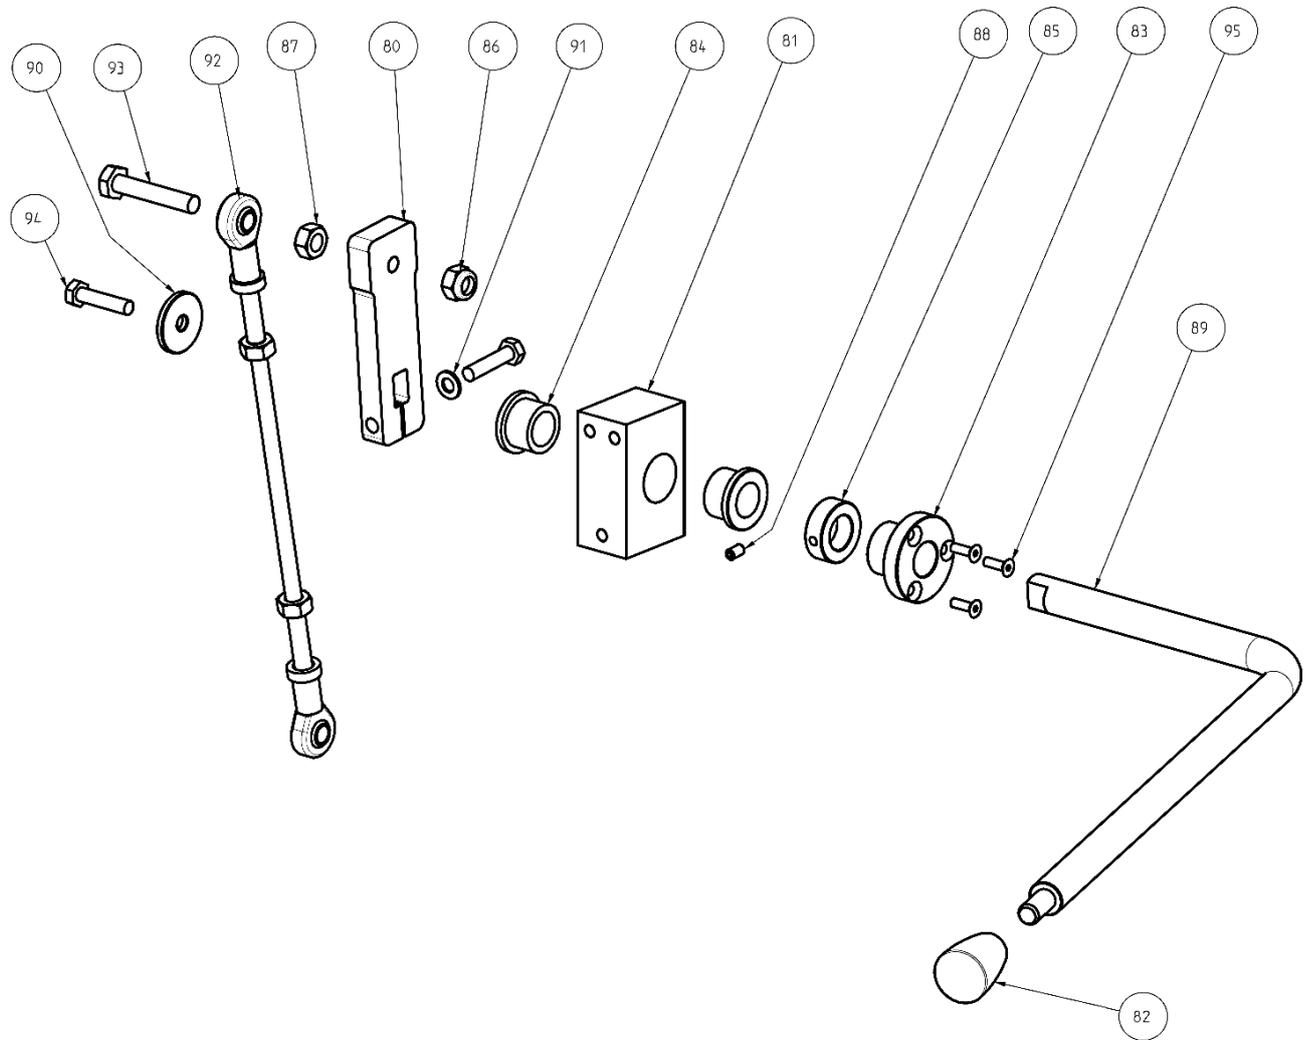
Gruppo sollevamento / Lifting assembly
